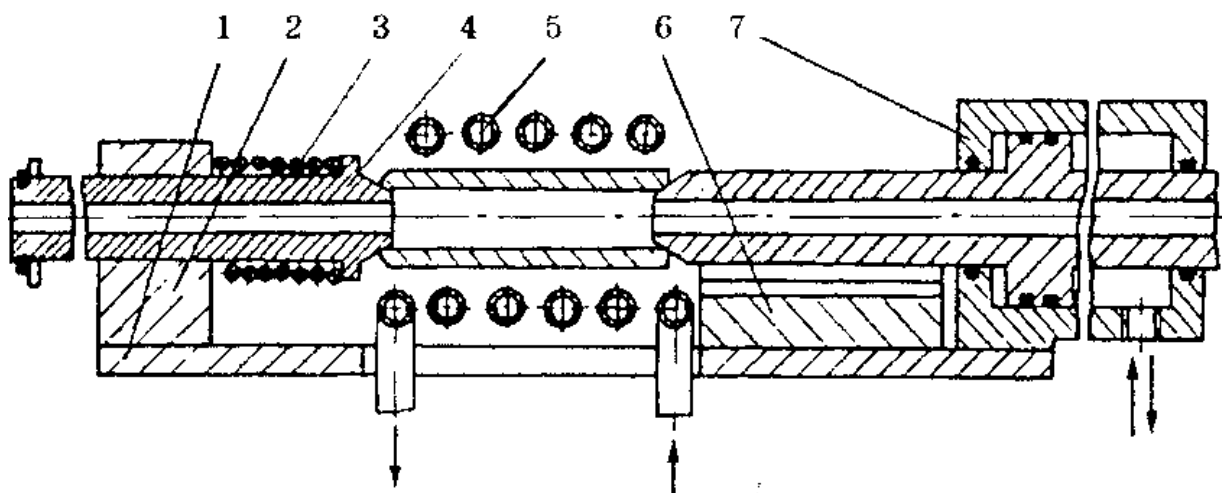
Схема стэнда для термопластичного роздавання поршневих пальців: 1-плита; 2- кронштейн; 3-пружина; 4-шток порожній; 5-індуктор; 6-призма на пряму; 7-пневмоциліндр
